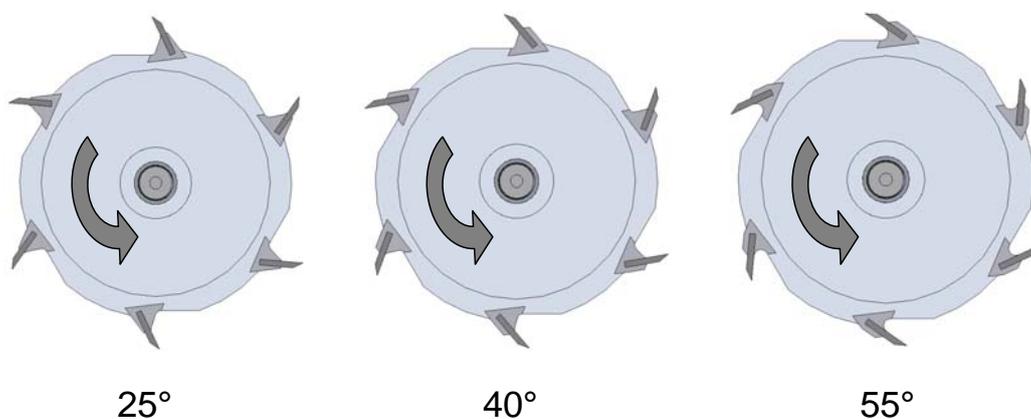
Vue de dessus de l'outil : différentes configuration d'angles de coupe
